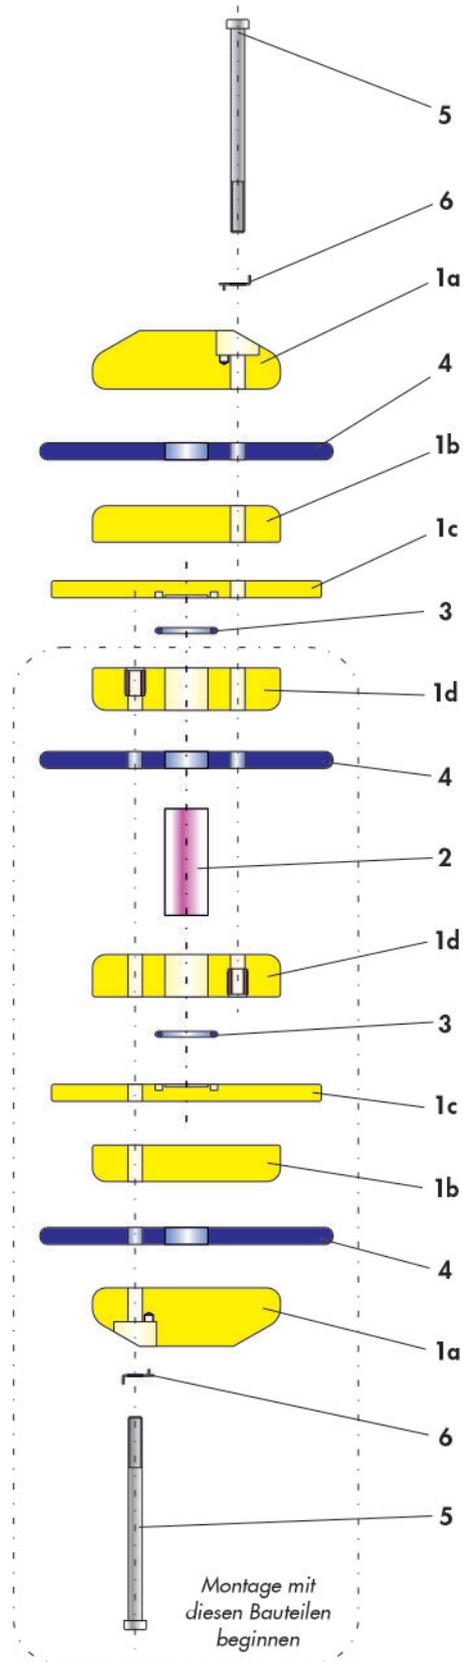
Explosionszeichnung des Molch TWIN 5
